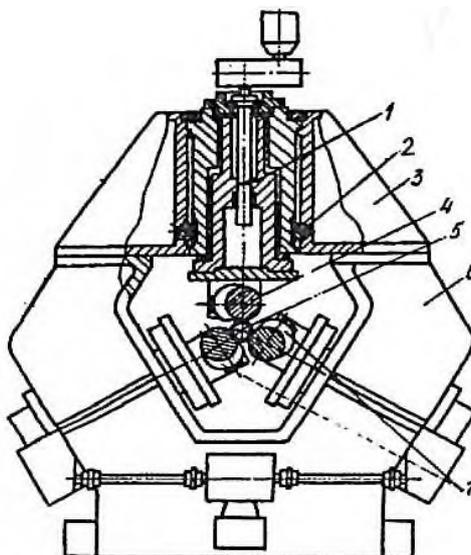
Схемы трубоправильных машин с одной двухвалковой обоймой [4]
